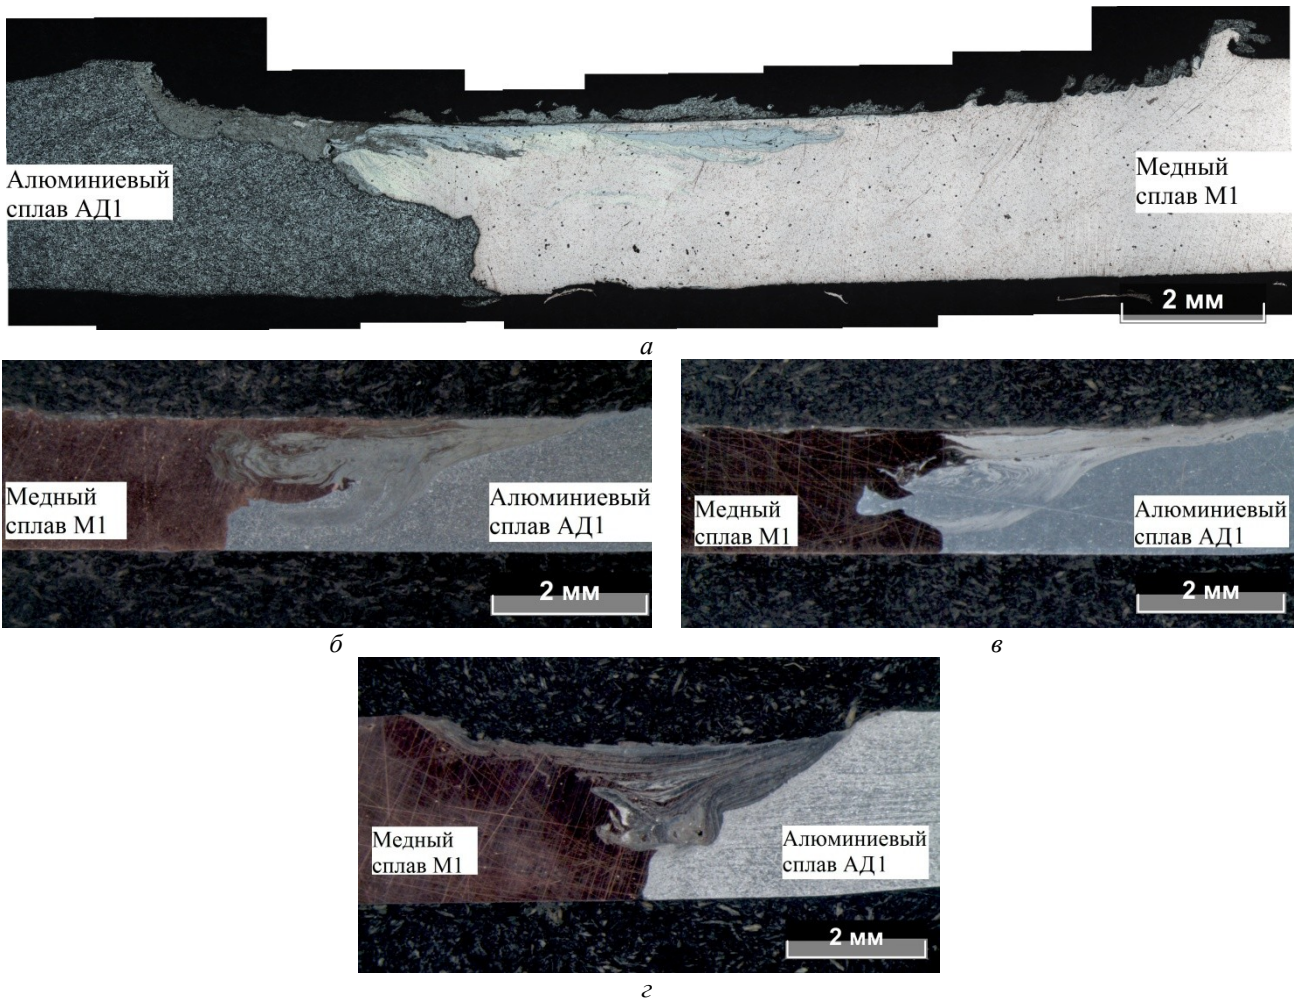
Макрошлифы сварных соединений с разными конструктивными типами кромок, выполненные с помощью СТП:
